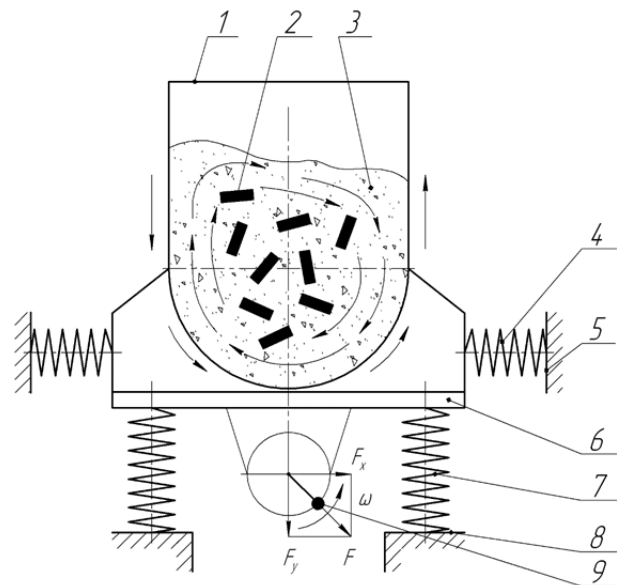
Принципова схема процесу віброобробки в резервуарі з «U» – подібною формою перерізу в площині коливаль: 1 – резервуар; 2 – оброблювані деталі; 3 – робоче середовище; 4, 7 – горизонтальна і вертикальна пружні підвіски; 5, 8 – жорсткі опори; 6 – віброплатформа; 9 – віброзбудувач
